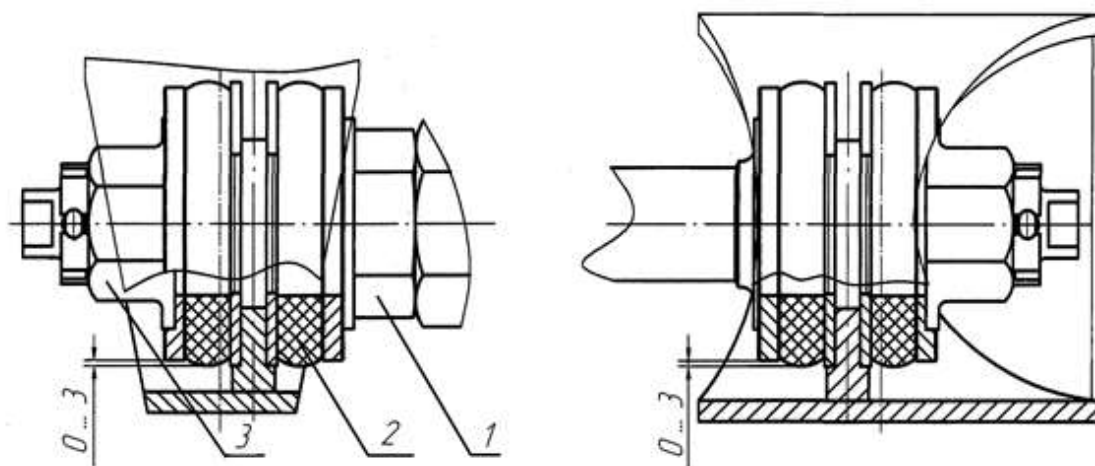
Резинометаллический пакет продольного поводка.
